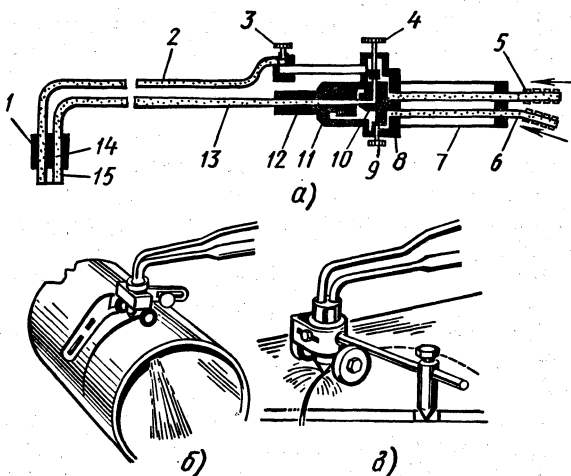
Ацетилено-кислородный резак (а) и приспособления для резки труб (б) и вырезки фланцев (в):
